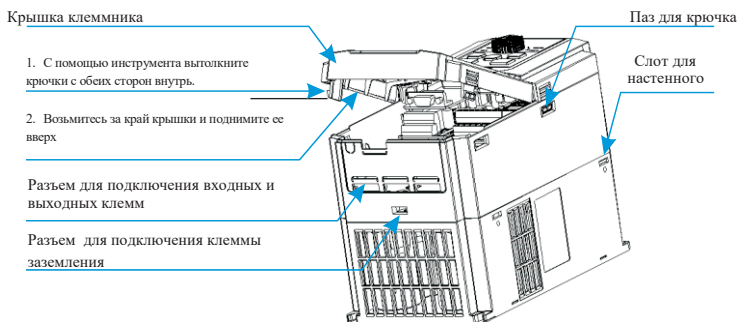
Чертеж снятия пластиковой крышки клеммного отсека корпуса
